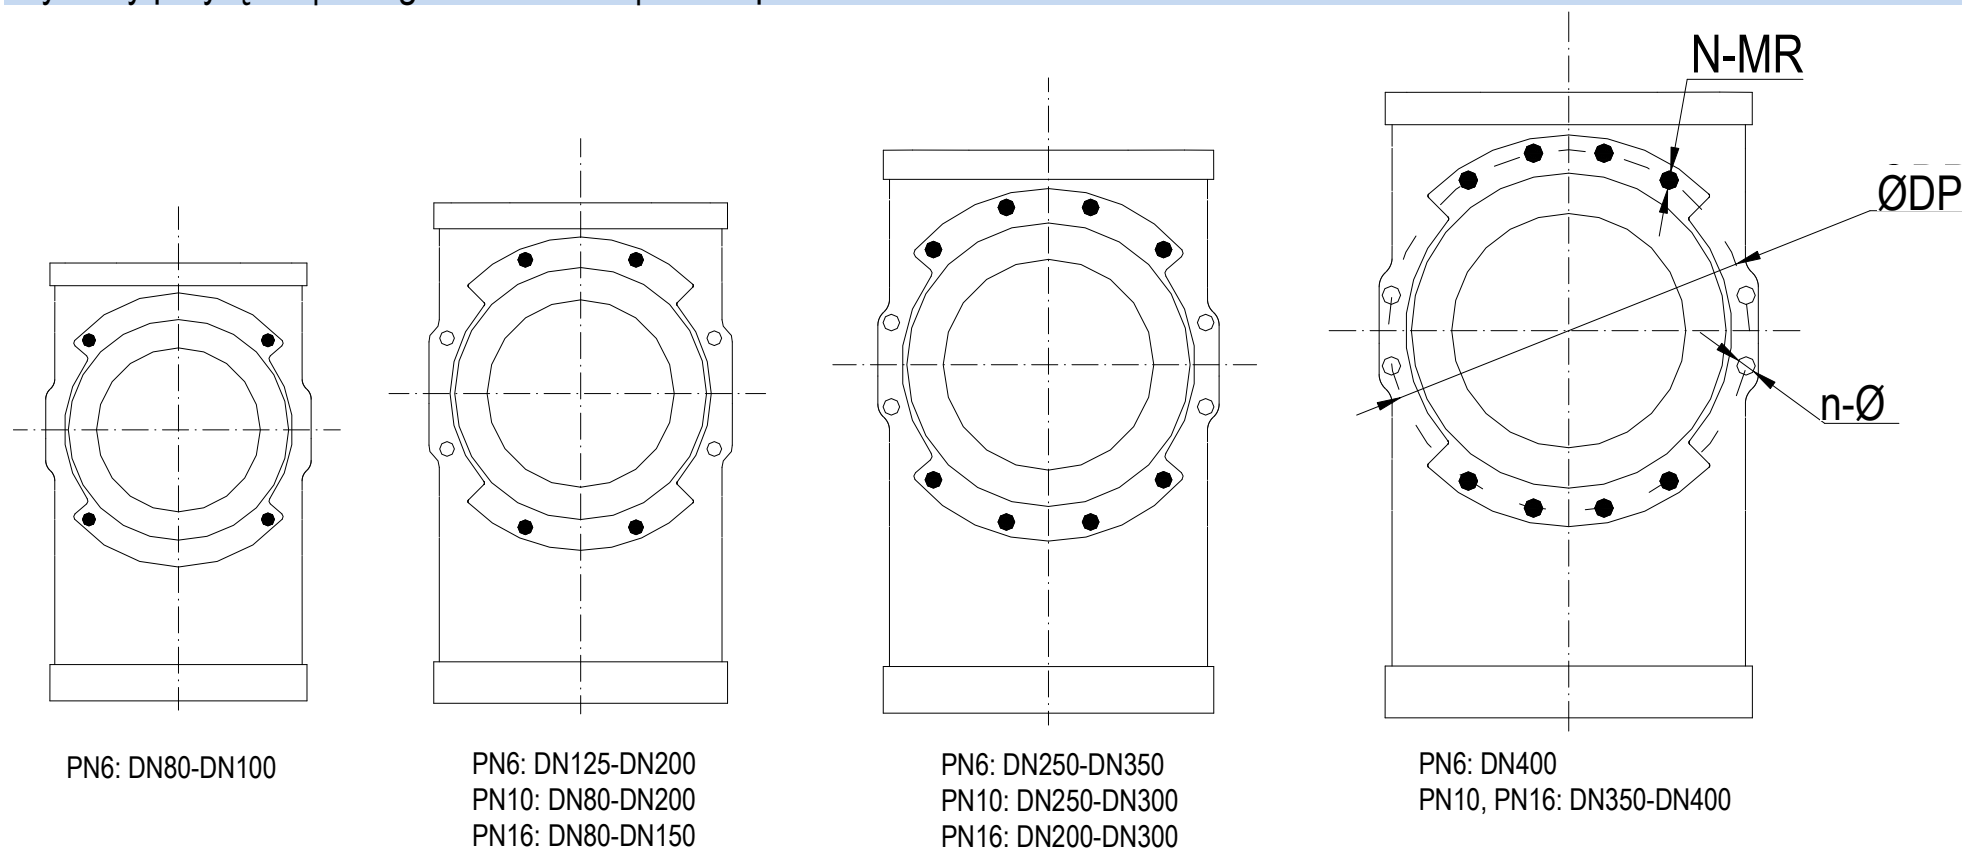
Główne wymiary urządzenia | Main device dimensions | Основные размеры устройства
